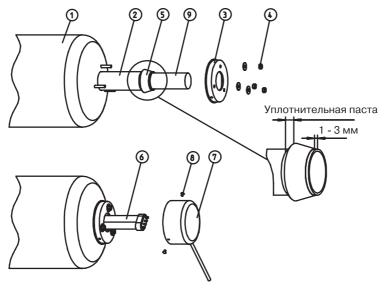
Монтажный чертеж для типов 40 S и 115 S
